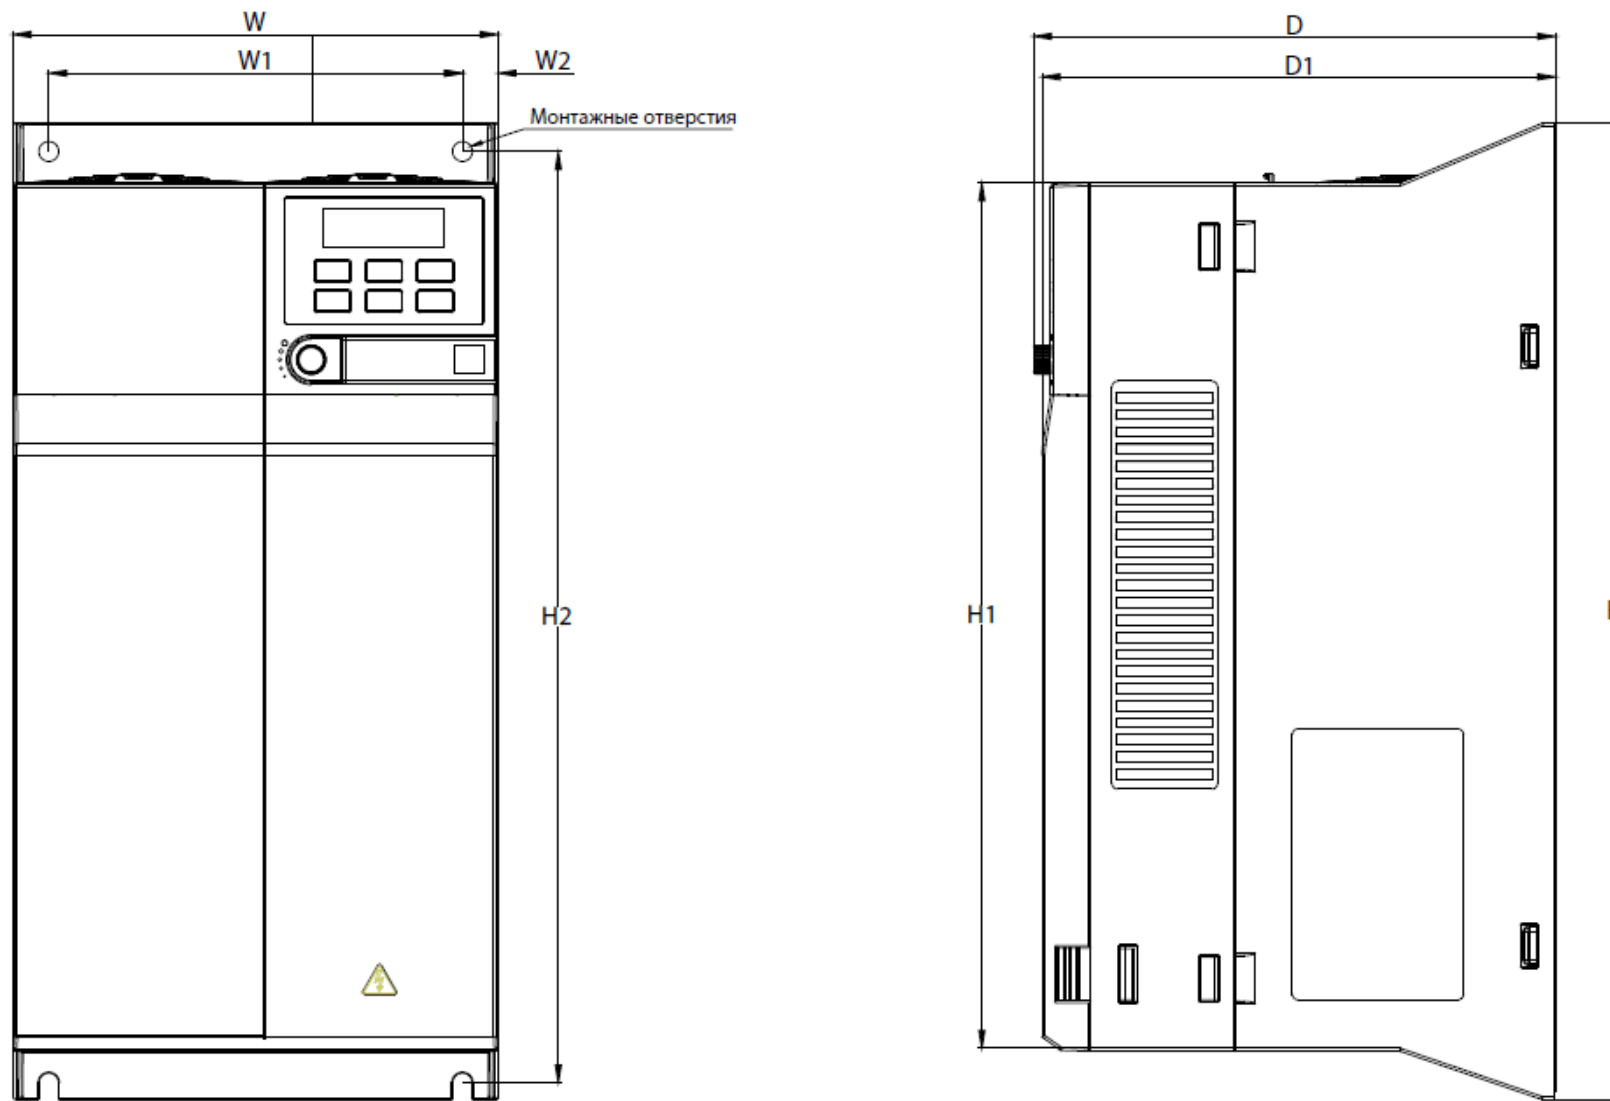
Чертеж преобразователя частоты типоразмер А4
